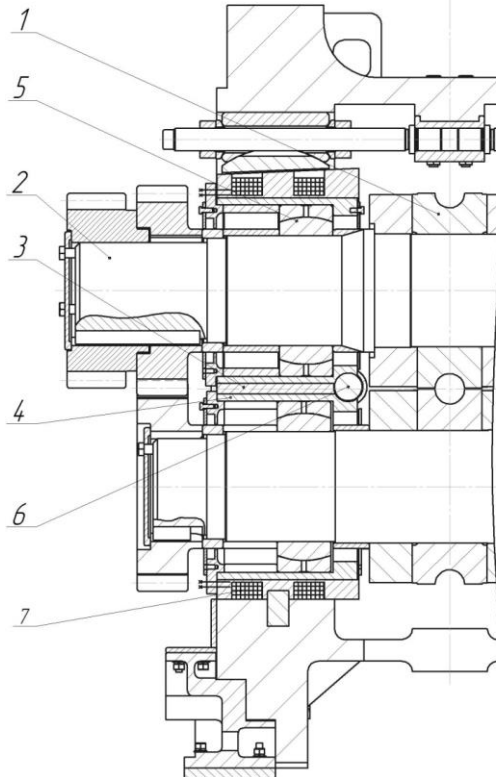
Конструкція робочої кліти стану ХПТ з суцільними намотаними подушками: 1 – калібр, 2 – робочий валок, 3 – корпус подушки, 4 – ексцентрикові втулки, 5 – підшипники, 6 – черв'як, 7 – намотка із надміцного матеріалу
